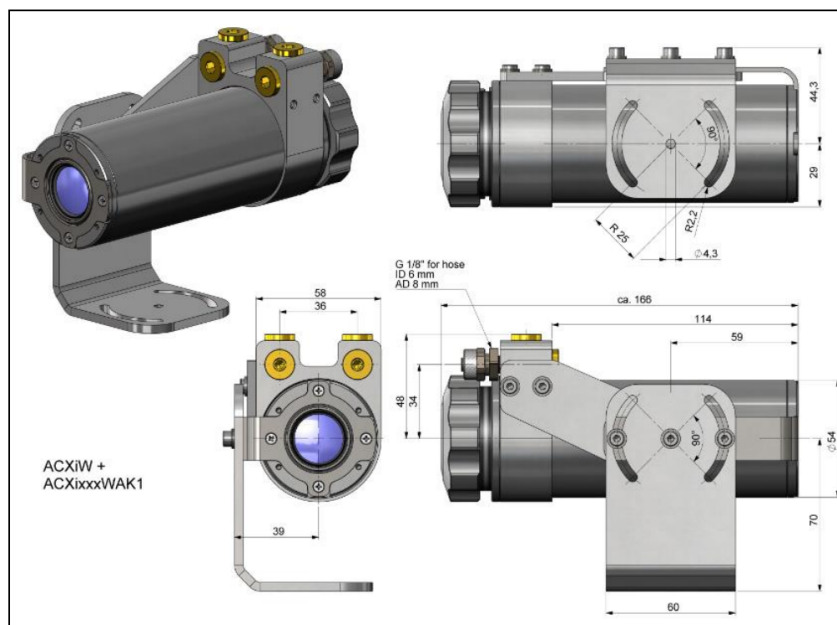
water cooling acoplado a la cámara Optris, dimensiones (mm).
